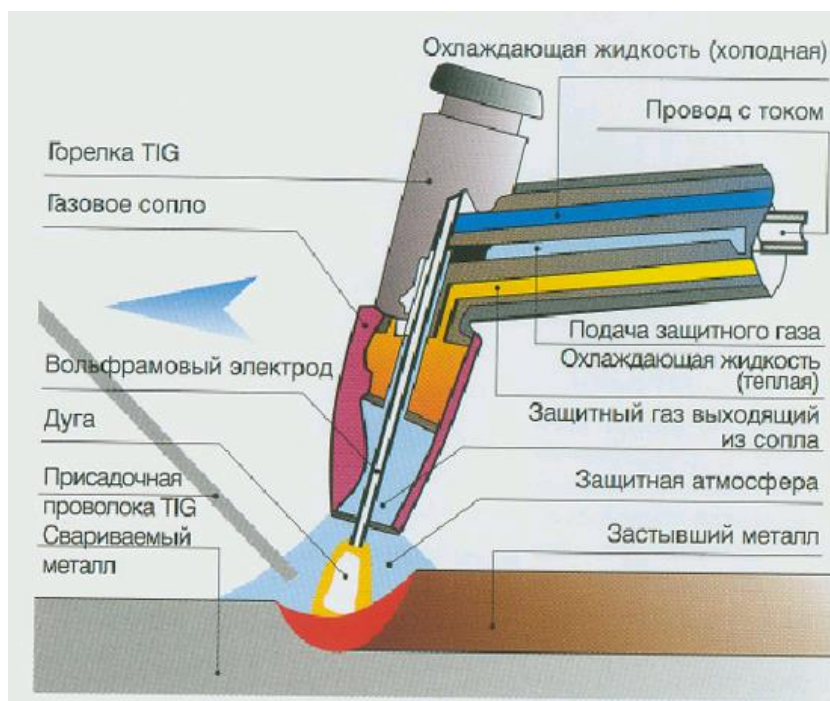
Схема сварки неплавящимся электродом в инертном газе
